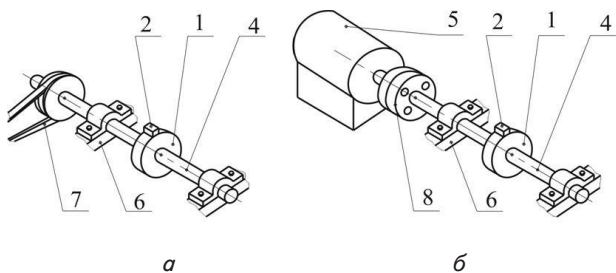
Двухчастотный вибровозбудитель, приводящийся во вращение при помощи: *а* – ременной передачи; *б* – муфты: 1 – корпус АБ; 2 – дебаланс; 4 – вал; 5 – электродвигатель; 6 – опора; 7 – ременная передача; 8 – муфта
